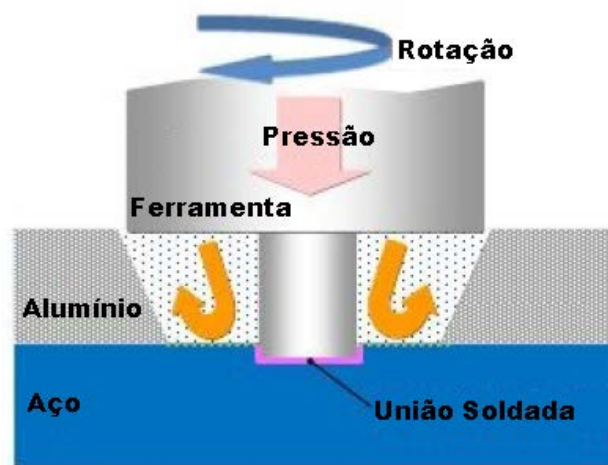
Seção transversal esquemática do processo de soldagem FSW utilizado para a soldagem do subchassi dos modelos Honda Accord produzidos a partir de 2013 [4].
